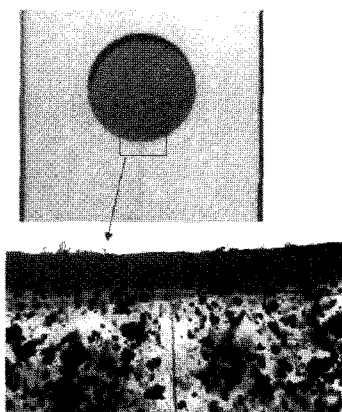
Weld line에서 다면체 입자의 분포.
